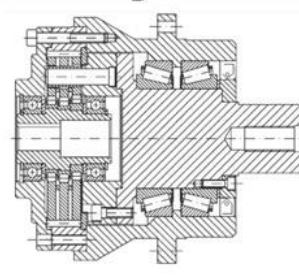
Конструкція планетарно-цивкового редуктора з 3 сателітами типу К-2Н-В
